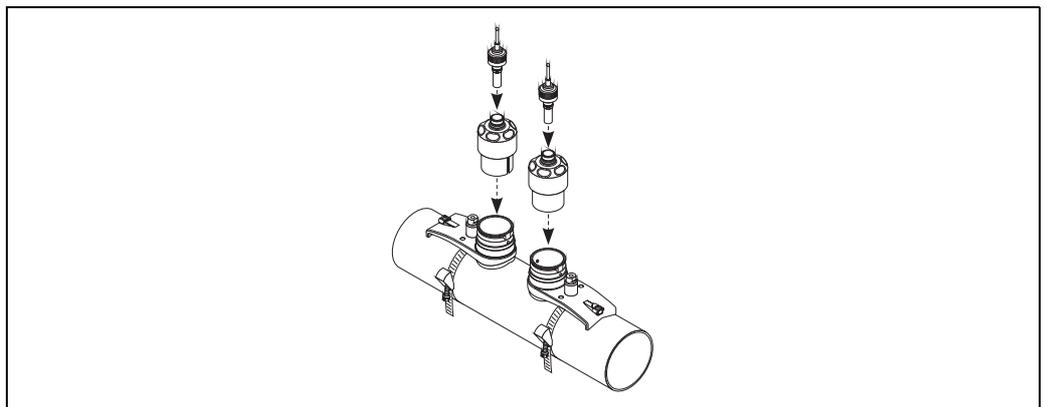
Montaggio del sensore e collegamento del cavo di collegamento
